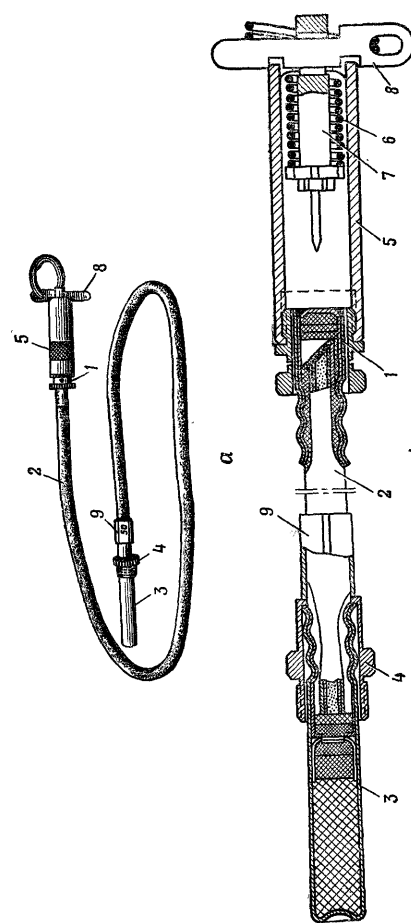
Зажигательная трубка с механическим воспламенителем: а — общий вид, б — разрез. 1 — воспламенительный узел; 2 — огнепроводный шнур; 3 — капсюль-детонатор № 8-А; 4 — ниппель; 5 — корпус; 6 — пружина; 7 — ударник; 8 — чека с кольцом; 9 — глубокая прорезь, предназначенная для установки чеки в предохранительное положение; 10 — мелкая прорезь, предназначенная для перевода чеки в рабочее положение.
